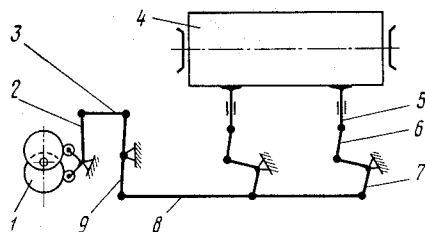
Схема кулачкового зевобразовательного механизма станка СТБ
